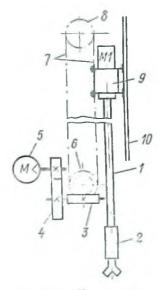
Кинематическая ехема вращательно-подающего механизма с цепной подачей бурового станка СБУ-125-24
